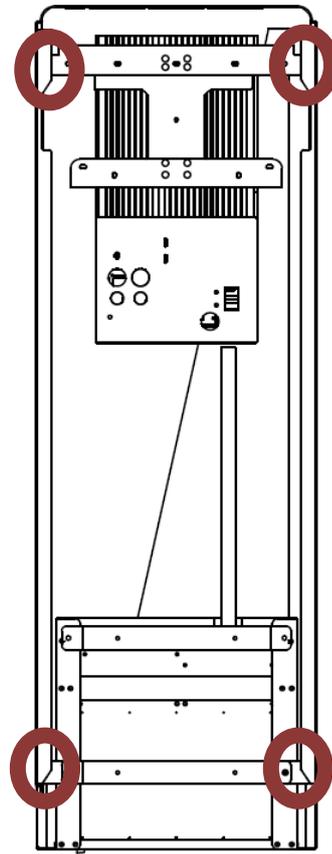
Vista de la tapa posterior, bridas cubiertas.
